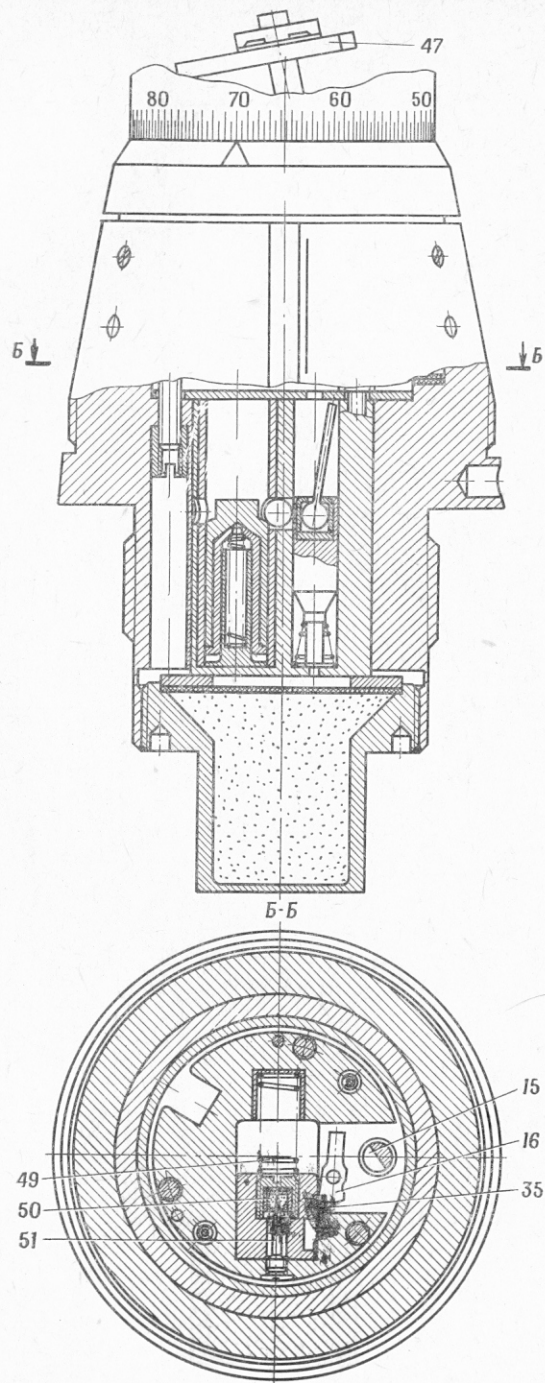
Трубка ГДТ-90 (положение деталей при срабатывании):
